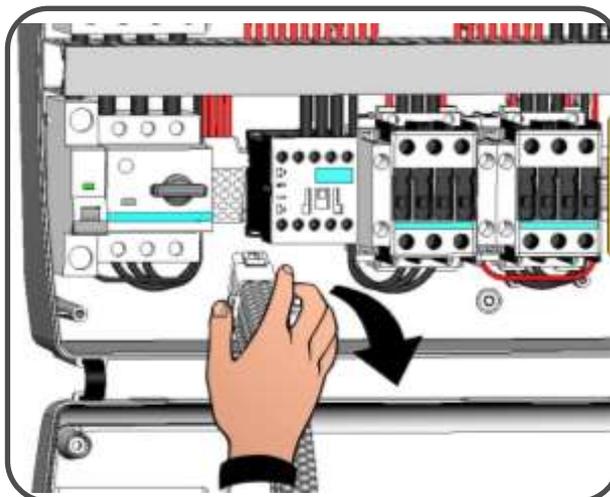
Ejerza presión sobre lodos de cada bisagra para extraerla de su sede y extraiga completamente el frontal.
